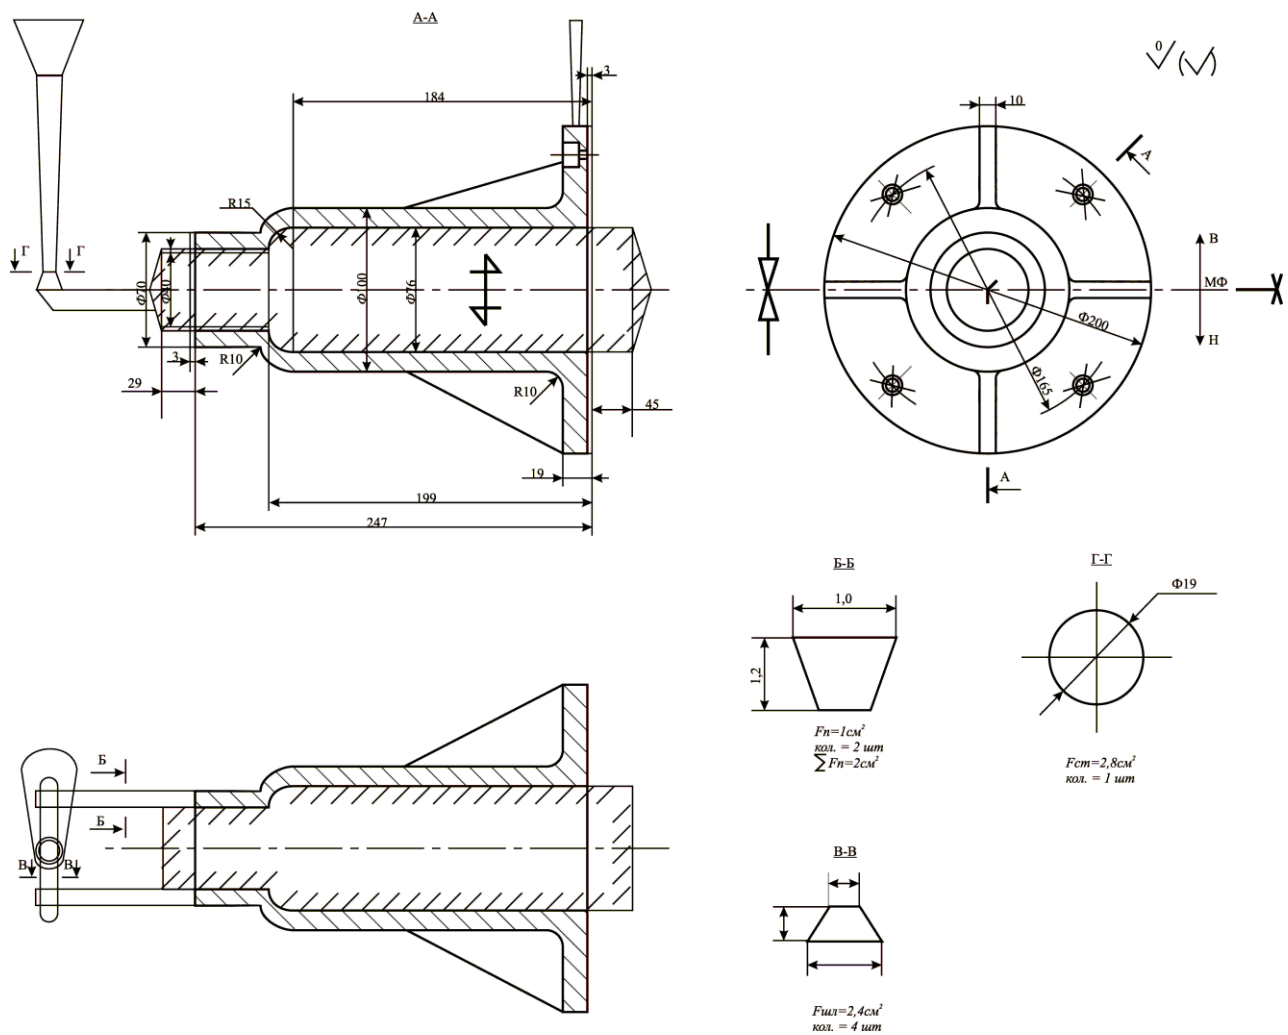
Ливарні технологічні вказівки на кресленні деталі:
